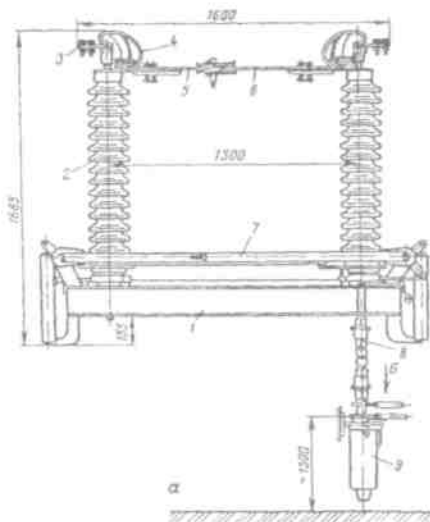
Разъединитель горизонтально-поворотного типа РНДЗ-2-110: а — включенное положение разъединителя: 1 — рама; 2 — опорный изолятор; 3 — наколечник для присоединения шин; 4 — гибкая связь; 5 — главный нож с ламелями; 6 — главный нож без ламелей; 7 — заземляющие ножи; 8 — тяга к приводу; 9 — привод
